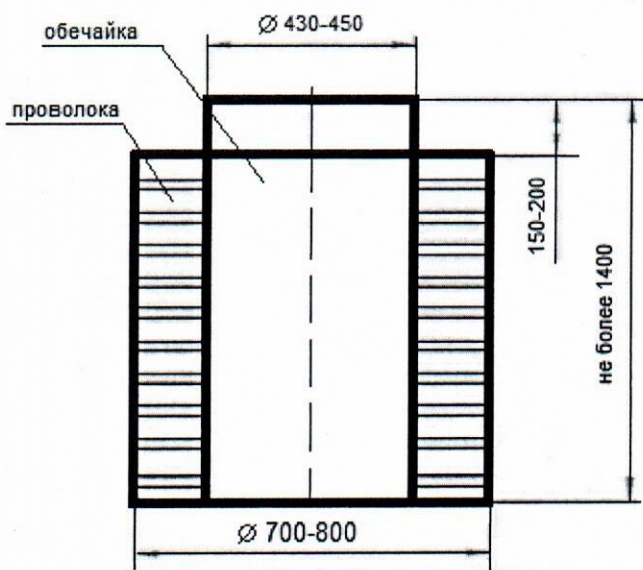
Схема упаковки со сварочной проволокой
